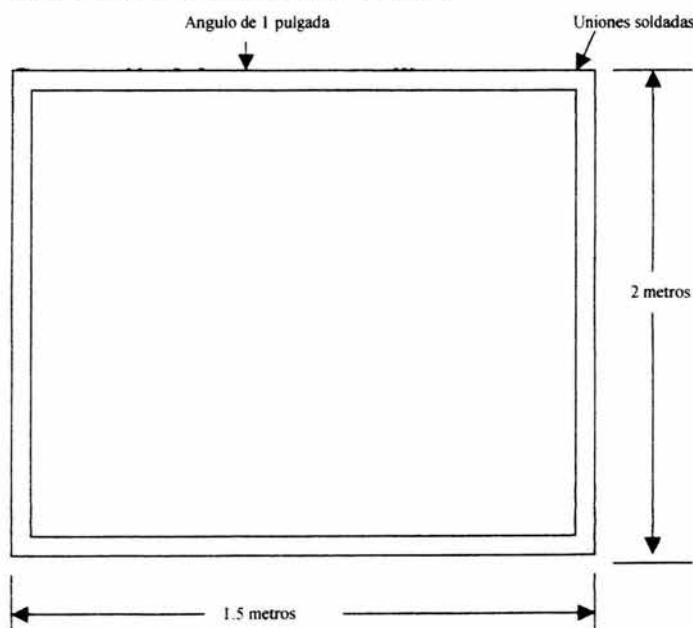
Soporte vertical de la estructura metálica (visto de frente).
